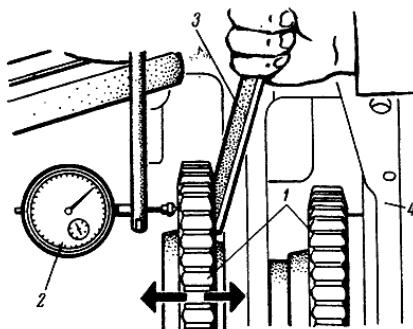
Проверка осевого зазора в подшипниках вторичного вала коробки передач МТЗ: 1 - вторичный вал; 2 - индикатор; 3 - монтажный ломик; 4 - корпус КПП
